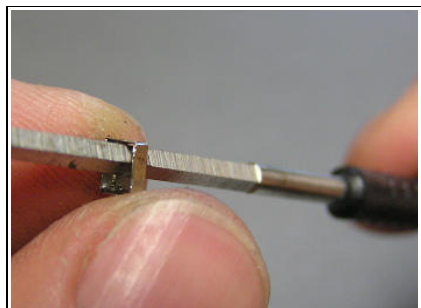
Die Bohrung auf 2,5mm aufreiben oder bohren. (Bunddurchmesser des 1:5 Getriebemotors). Siehe Abb. 22
